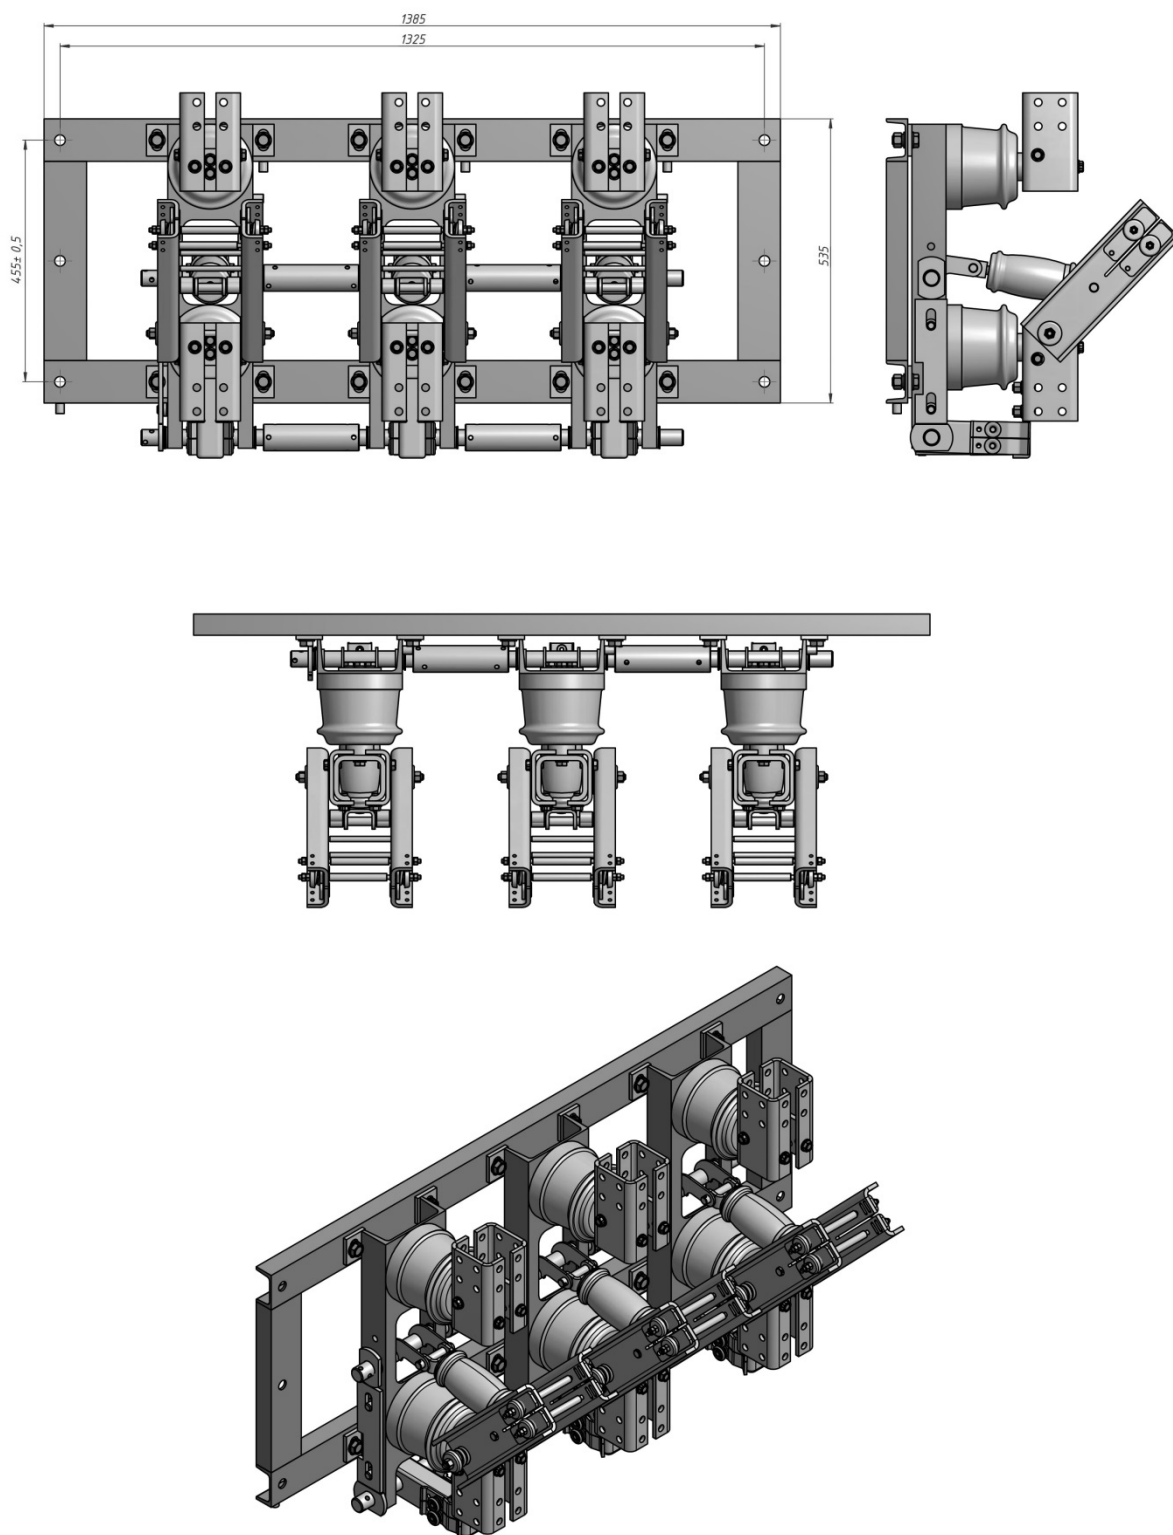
Габаритно-установочные размеры и устройство разъединителя PBR3
